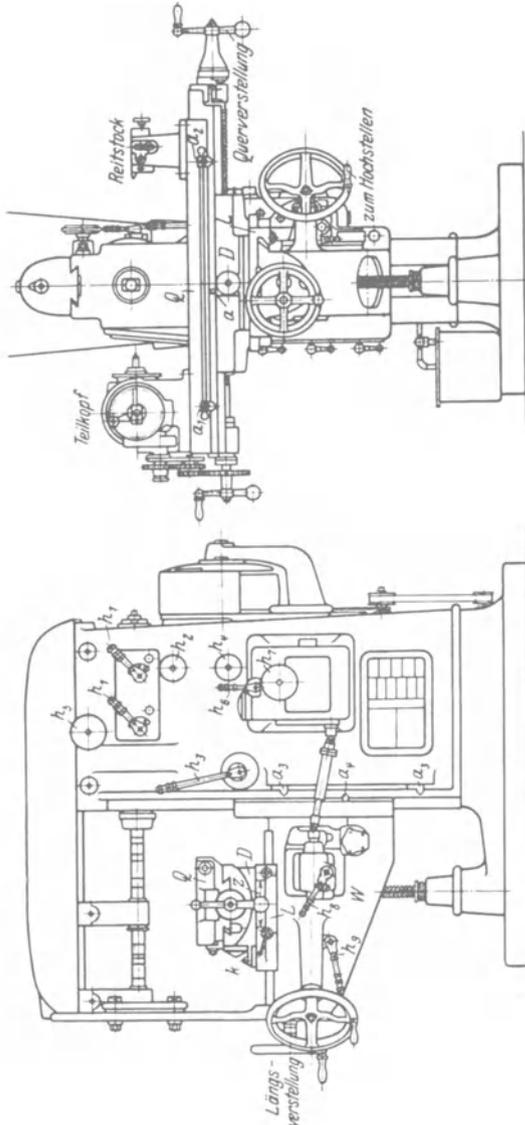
u. 279. Allgemeine Fräsmaschine.
